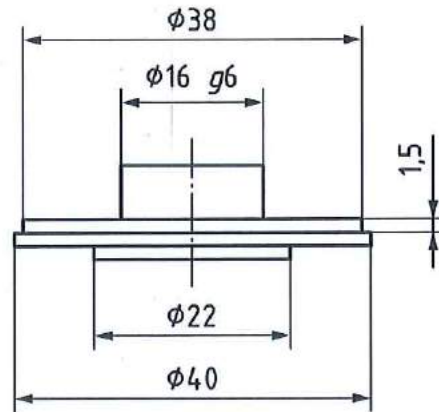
Insert de la chambre à cartouche pour Type 6,8/11
